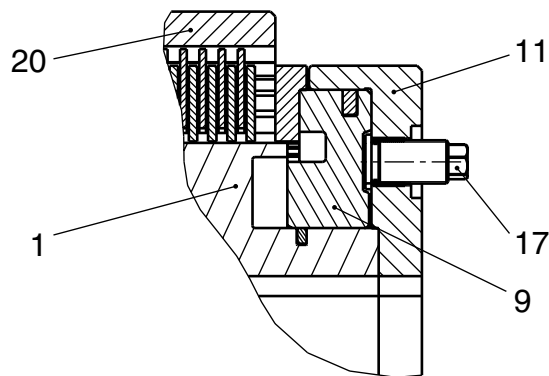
Variant 2 - Clutch with integral emergency engagement system
